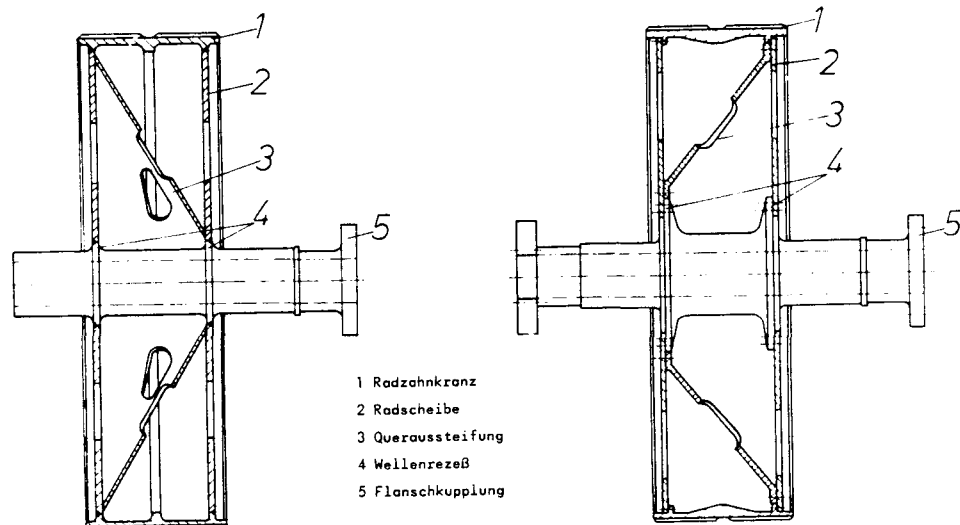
Befestigung von Getriebe-Großrädern auf hohlen Radwellen
